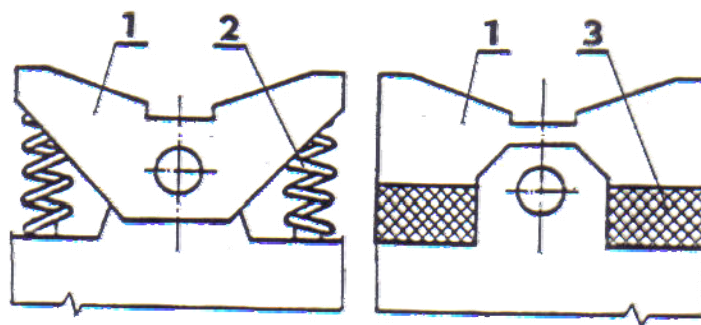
11 Konstrukční řešení typu MÚE dle obr. 4.1.2 – 6, 8
